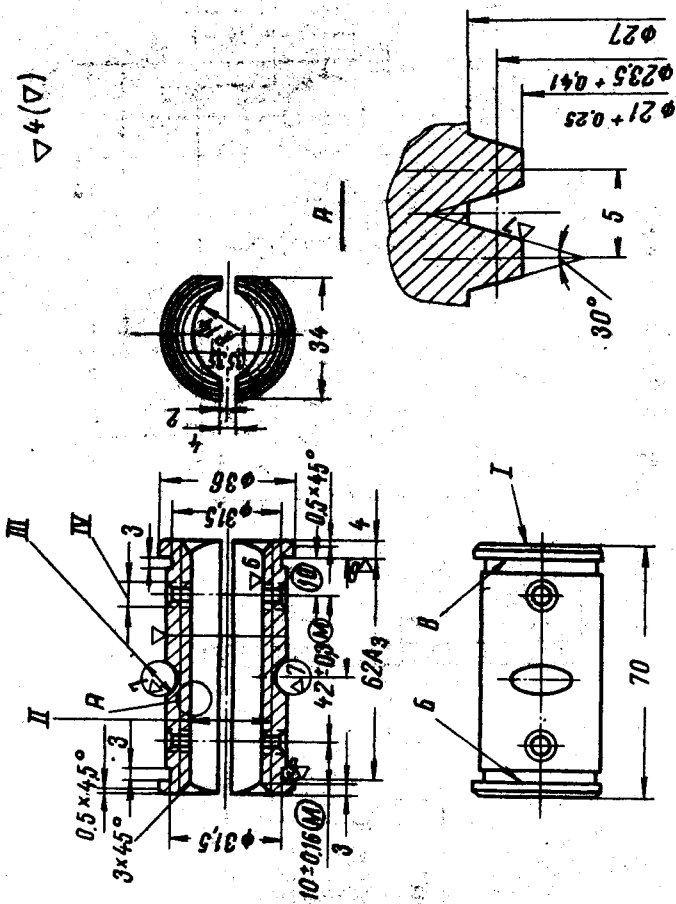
Гайка маточная, деталь № УОЩ.40.29:
